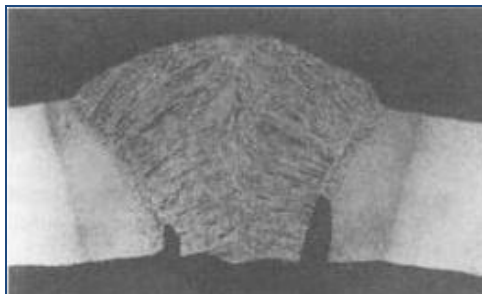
Grieta generada después del proceso de soldadura. [16]
